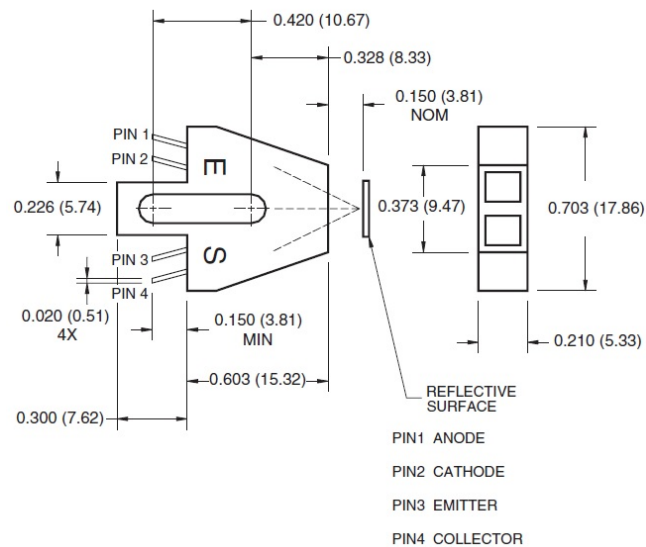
Dimensiones del encapsulado. Fuente [56].
